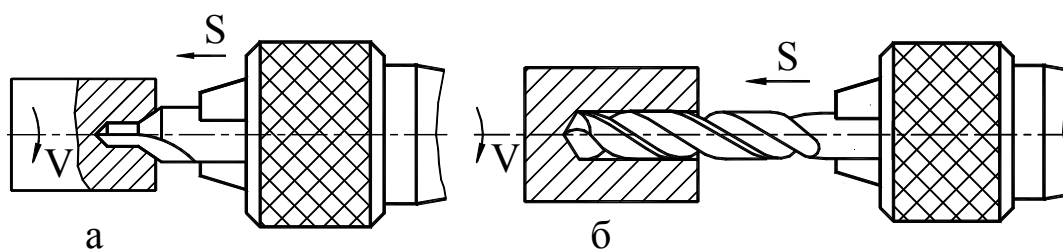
Сверление отверстий: а – центрование; б – сверление
